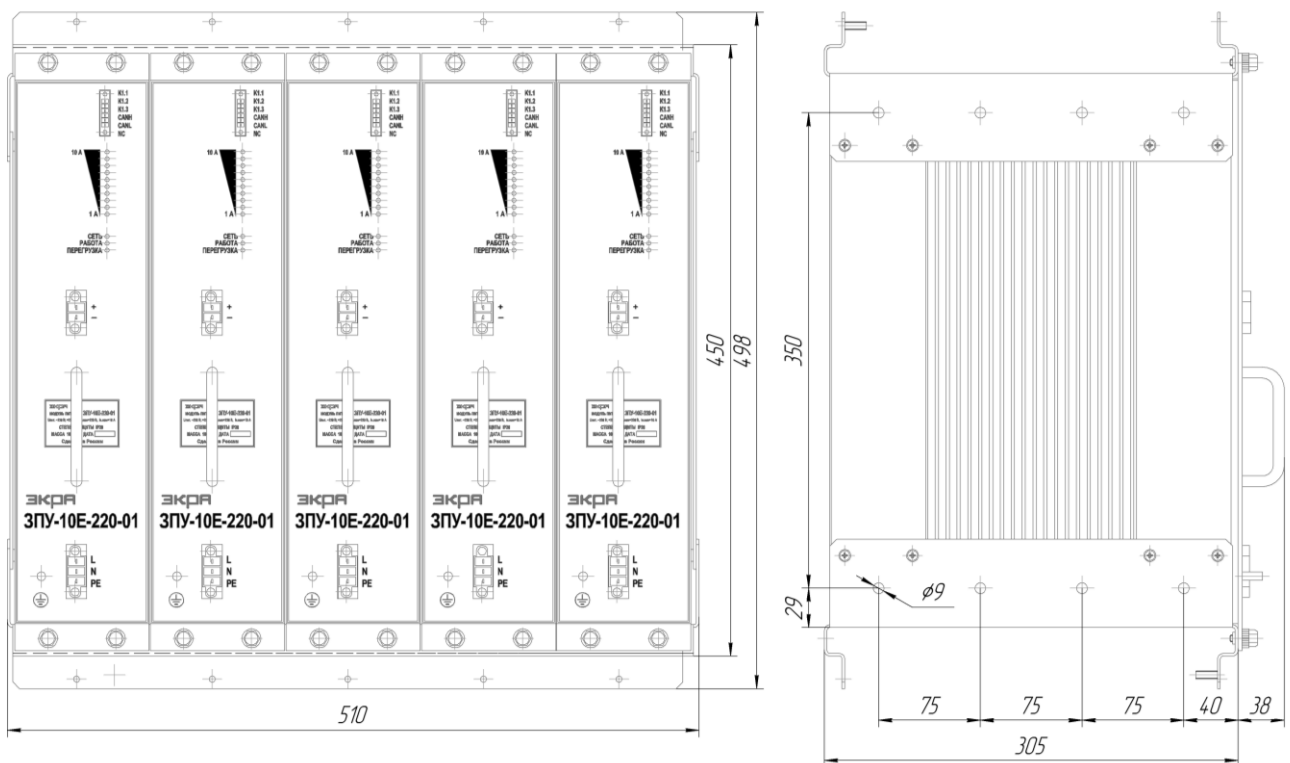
Габаритные размеры корзины ЗПУ-10Е
